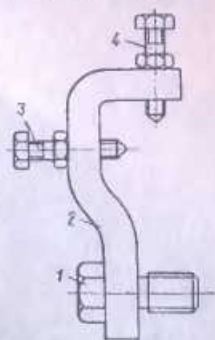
Приспособление для центровки дизеля с гребным валом или с валом гидротормоза:
